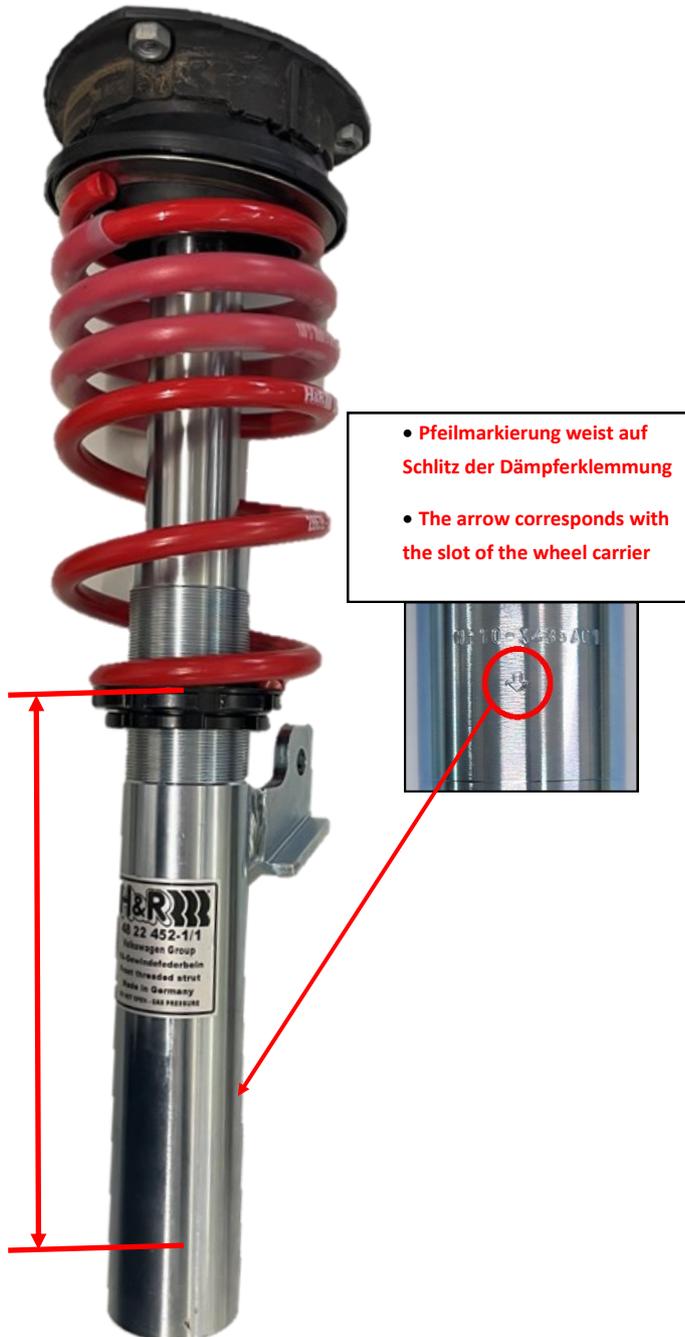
Markierung Einbauposition & Einstellmaß VA
